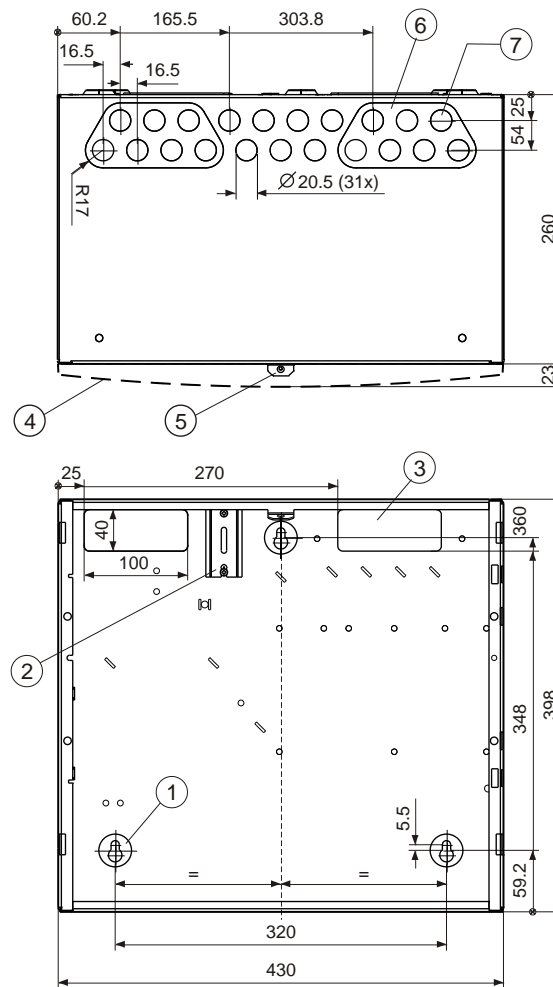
Dimensions boîtier (Large Extension) FH2004
